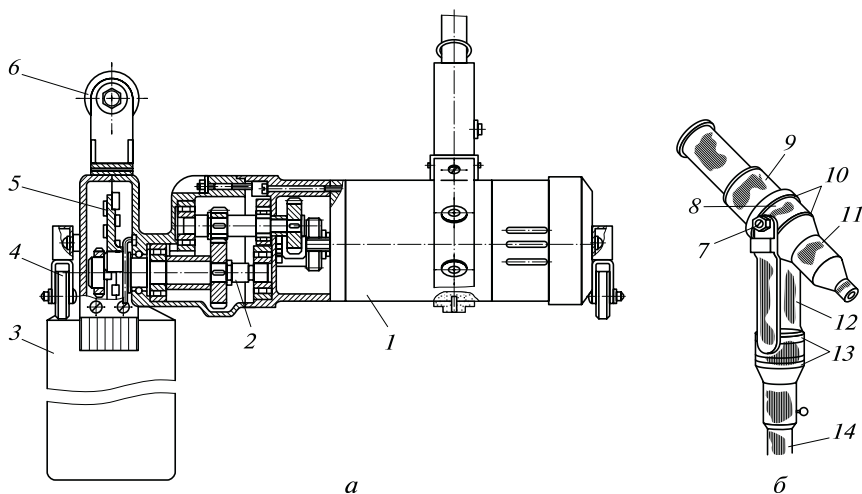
Механизмы для заготовки штраб и отверстий:
